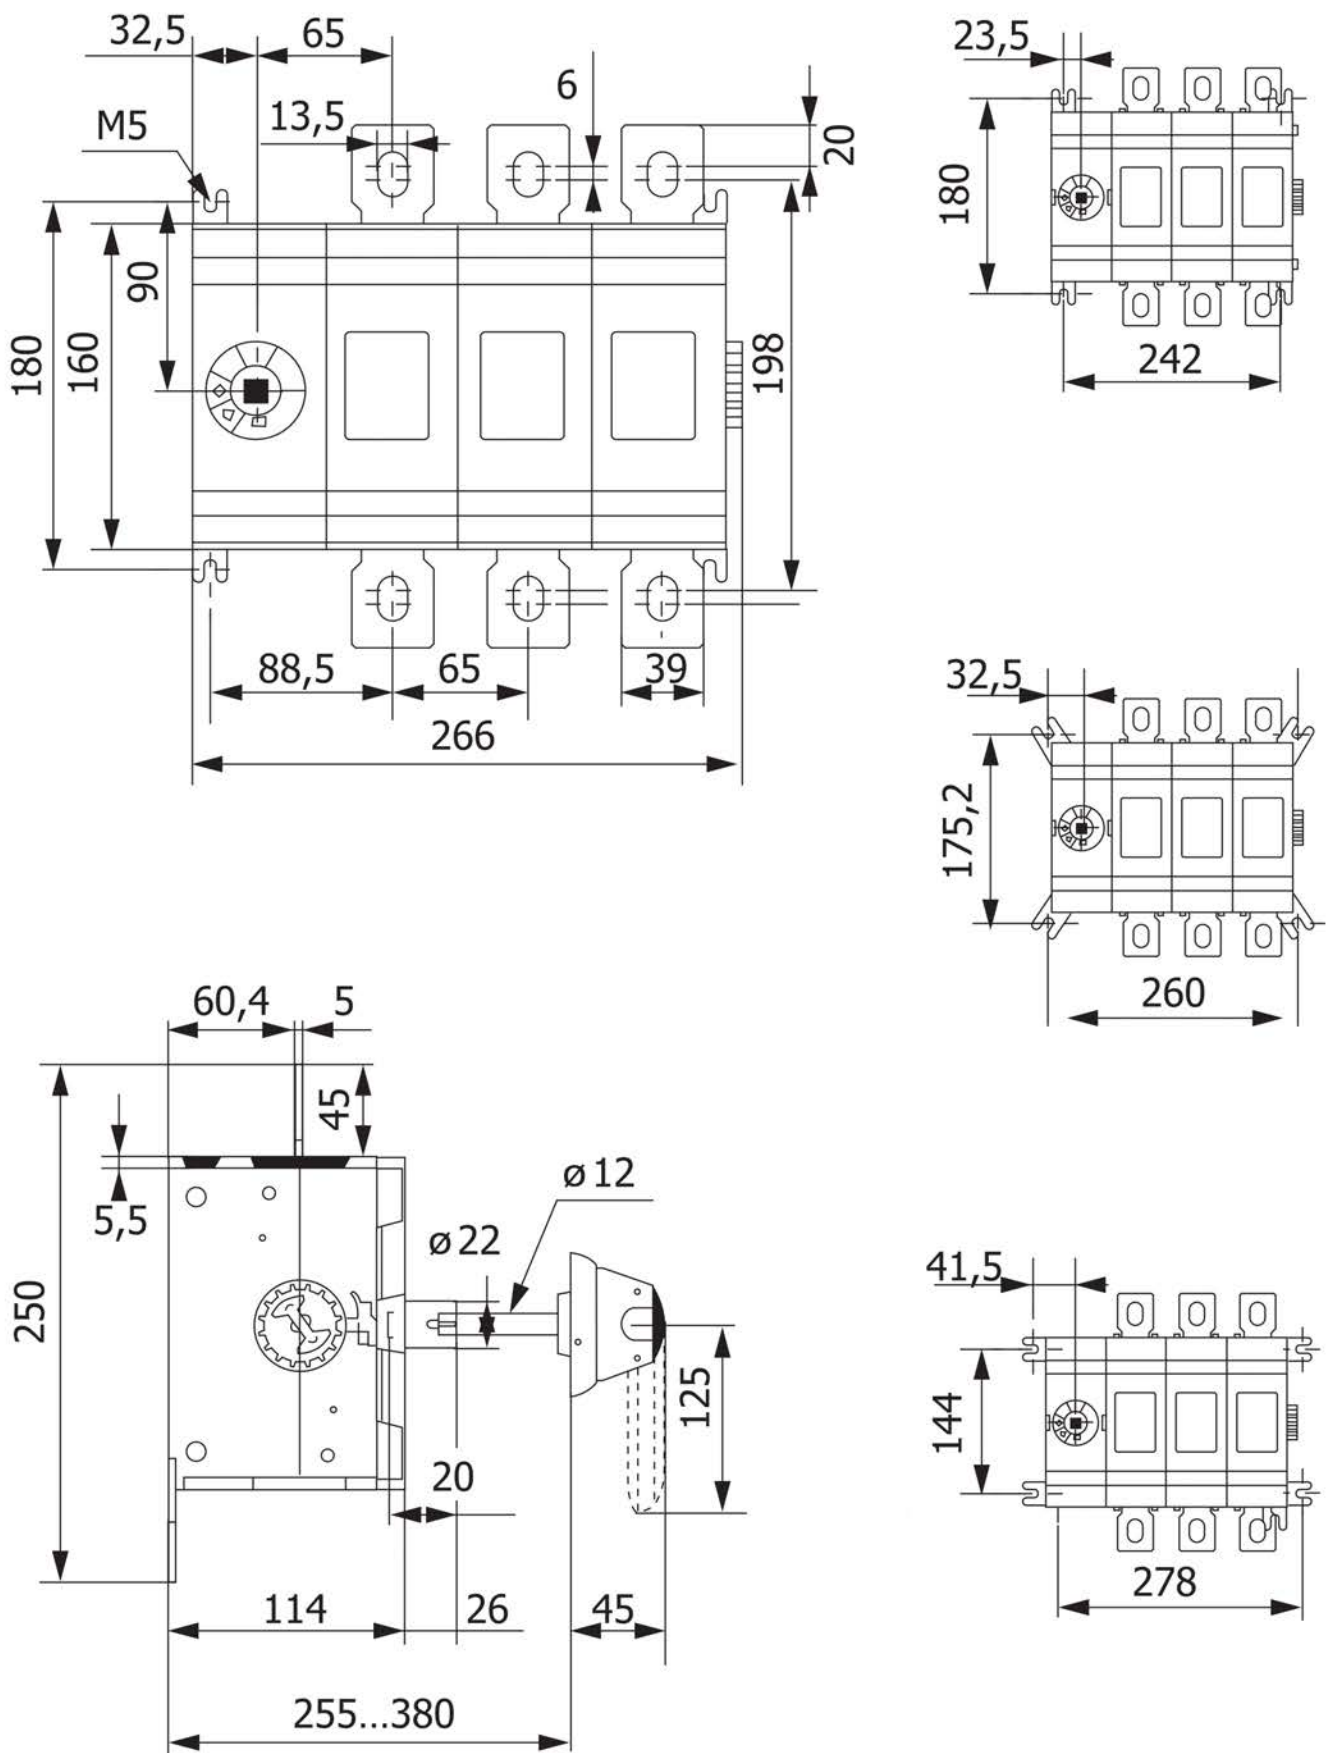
Габаритные и установочные размеры рубильников 600-800 А
